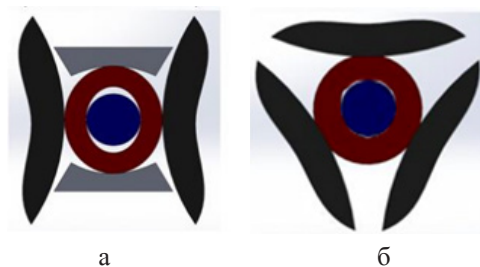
Деформация заготовки в двух- и трехвалковом станках
